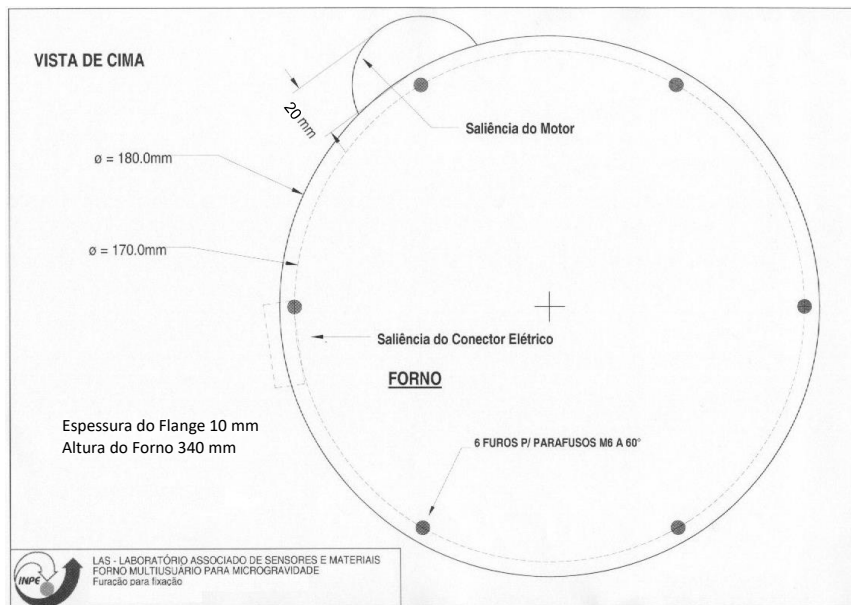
6. Detalhes dos pontos de fixação no flange superior e da posição do motor e conector de interface elétrica.
